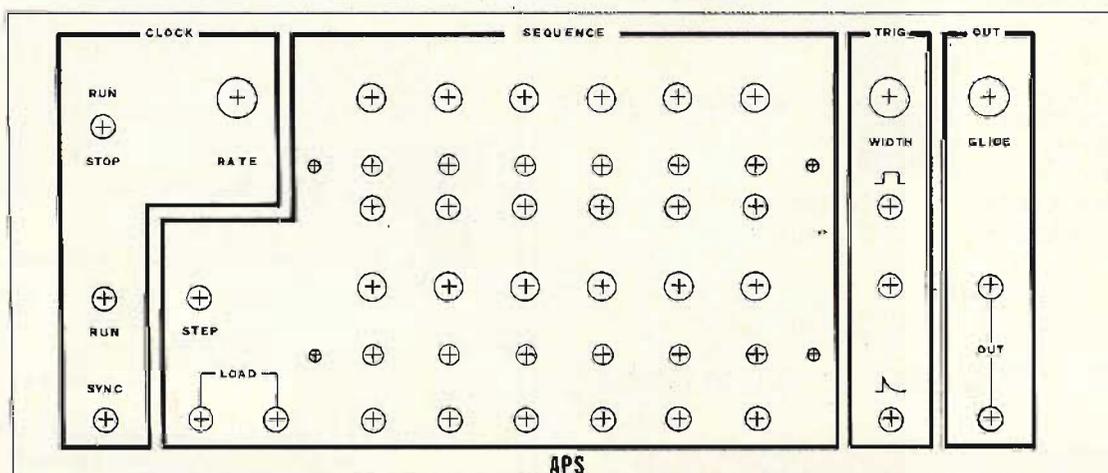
Disegno del pannello frontale in scala 1 : 2.
